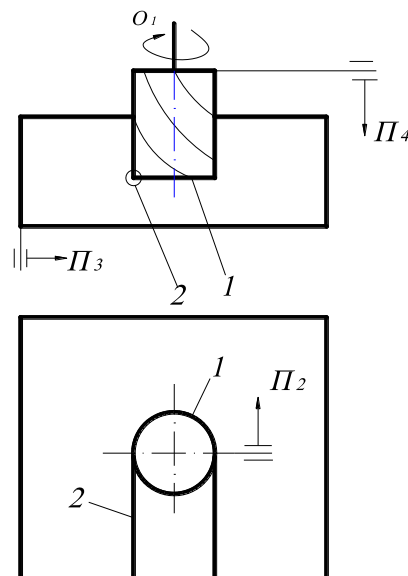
Схема фрезерування паза кінцевою фрезою
